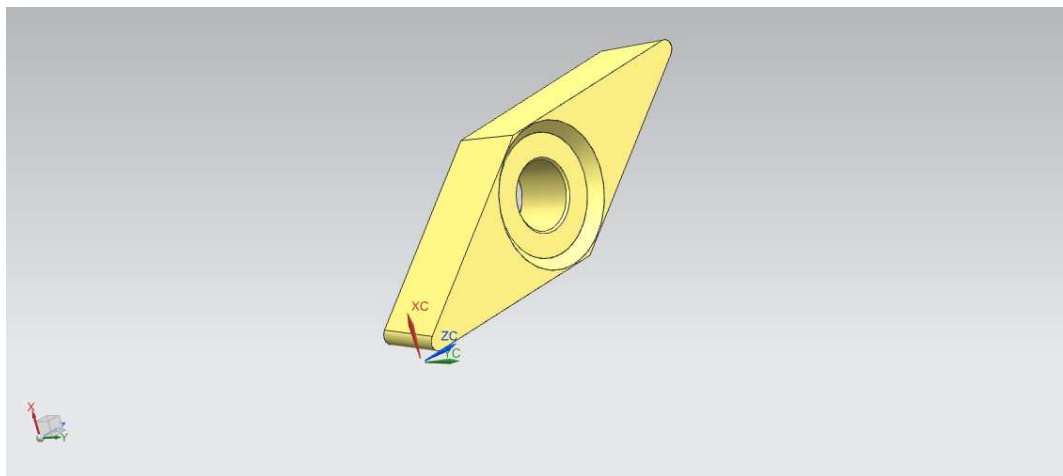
Sketch VBD typu VCMT 110304E-UM
